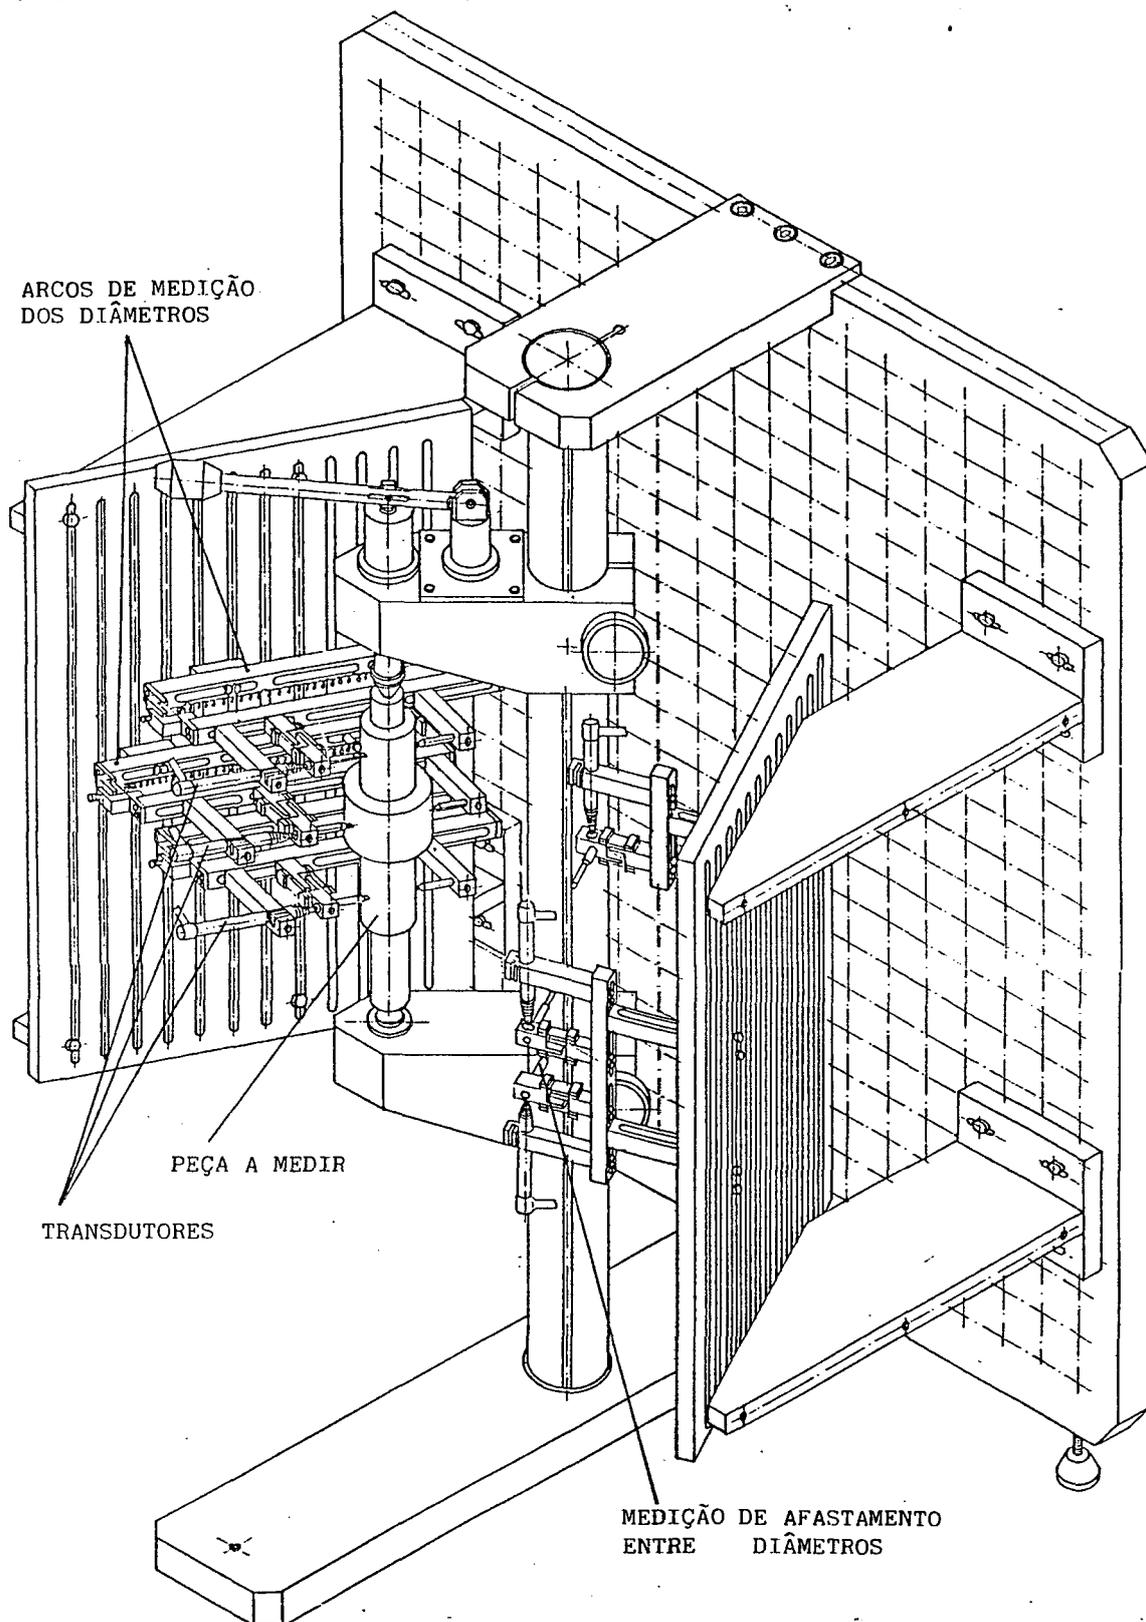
Dispositivo para medição de peças cilíndricas do conjunto modular [75].
